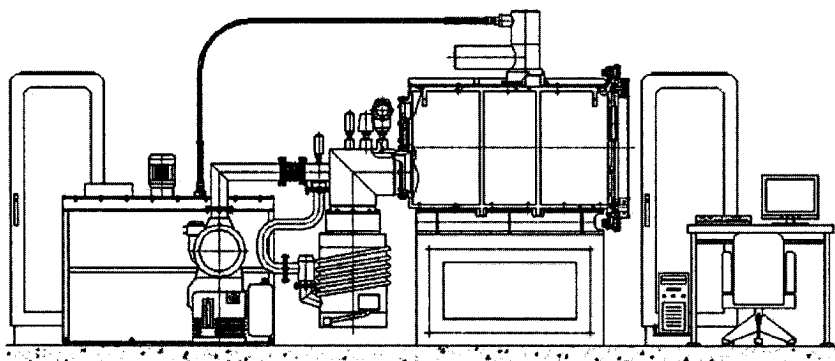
Схема електронно-променевої зварювальної установки ЕЛТУ-60.15/1.1
